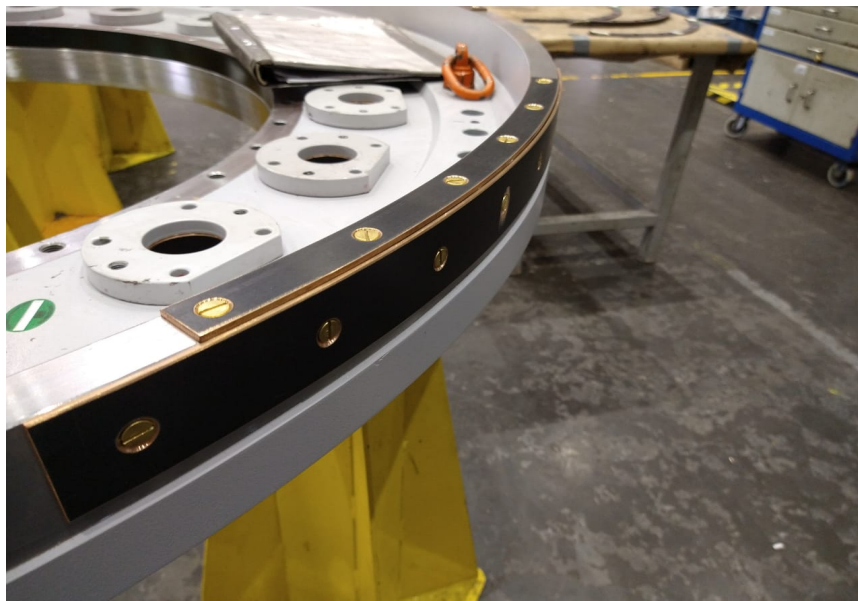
tampa do lado oposto à regulagem montada na caixa espiral
